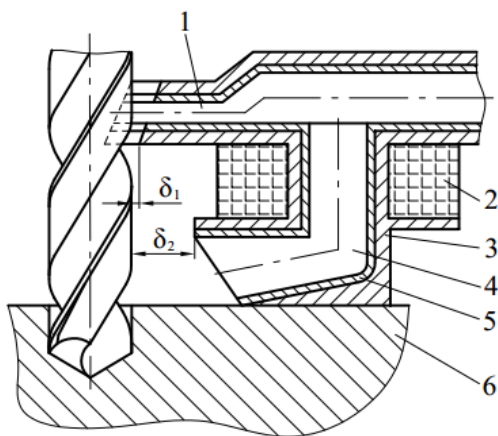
Схема комбінованого пристрою для видалення стружки
